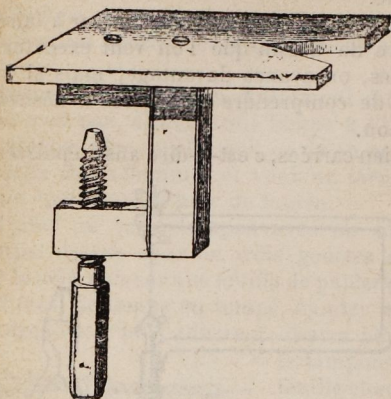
Presse placée sous le plateau de la machine à découper.
